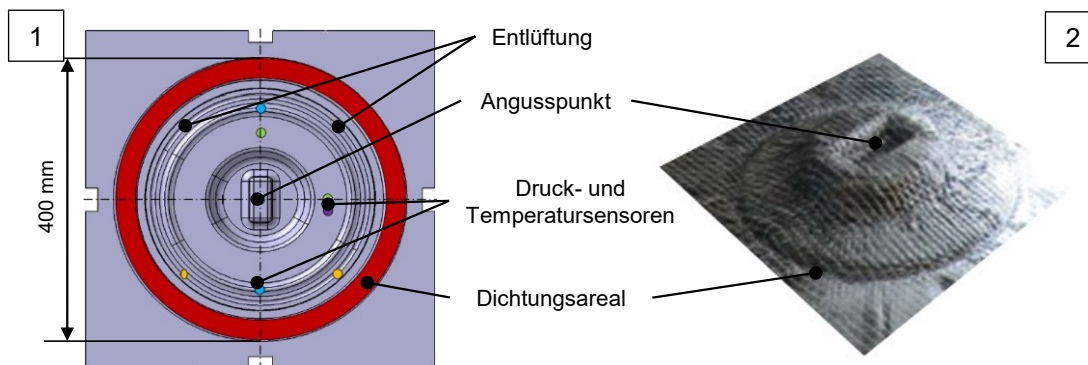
Versuchswerkzeug „Schikane“: Aufsicht Werkzeugkavität (1) und Ansicht Preform (2).
